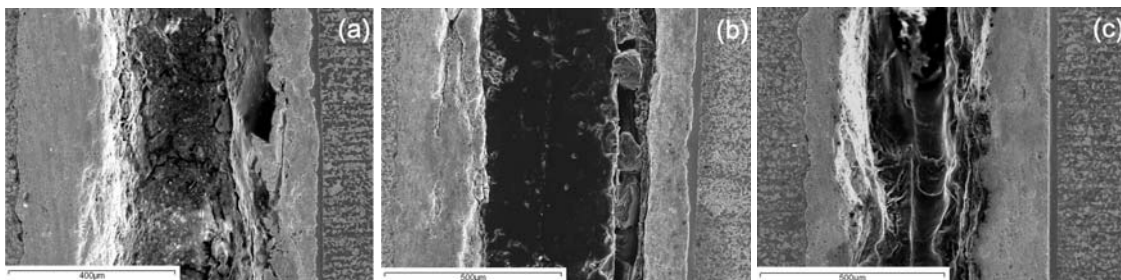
Sección transversal de la fractura obtenida de las uniones realizadas mediante ciclos de soldadura (a) estáticos, (b) dinámico 1 y (c) dinámico 2 en el acero AISI 1045.
